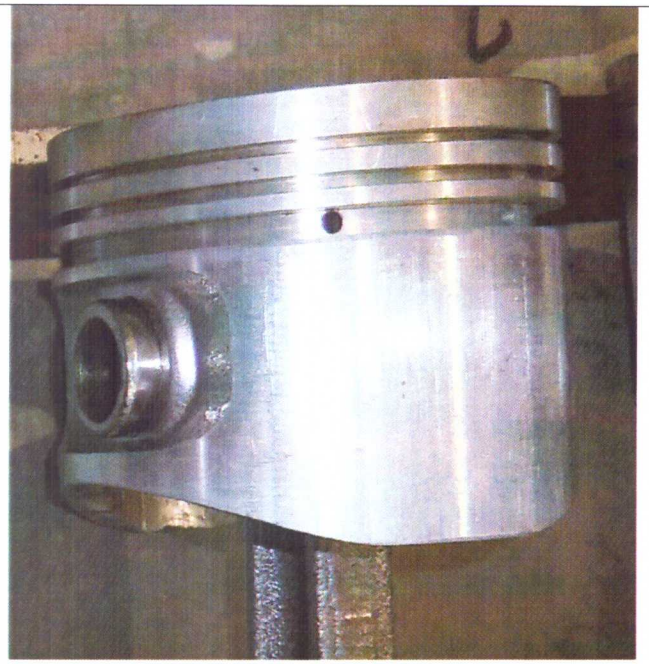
Внешний вид боковой поверхности поршня третьего цилиндра по окончании длительных испытаний двигателя при работе на базовом масле Castrol EDGE с добавкой нанокompозита Amortect PROOF
